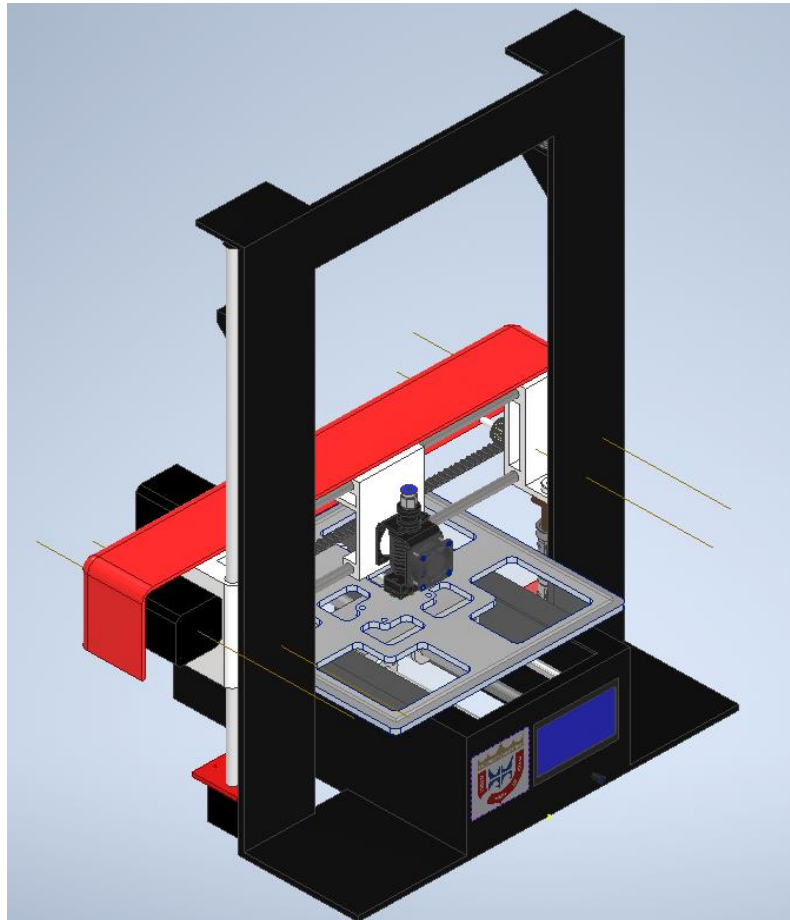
Vista isométrica del ensamblaje de la impresora 3D diseñada
